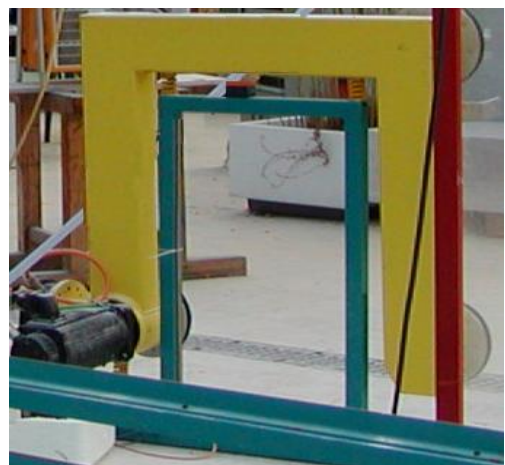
Frässpindel und Fräserkasten (links), Seilsäge (rechts)
